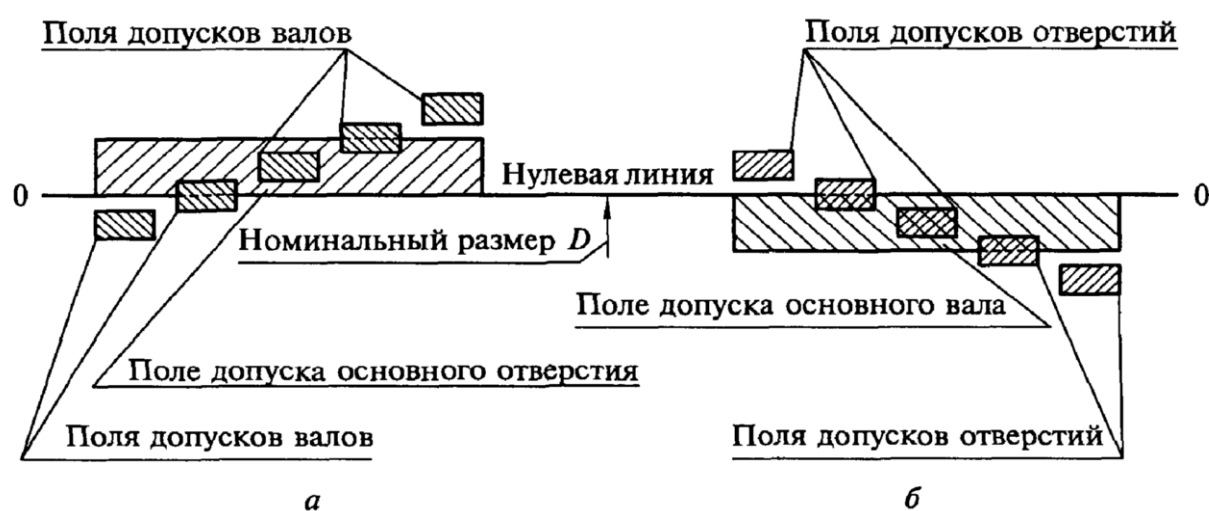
Примеры расположения полей допусков для посадок в системе отверстия и вала
